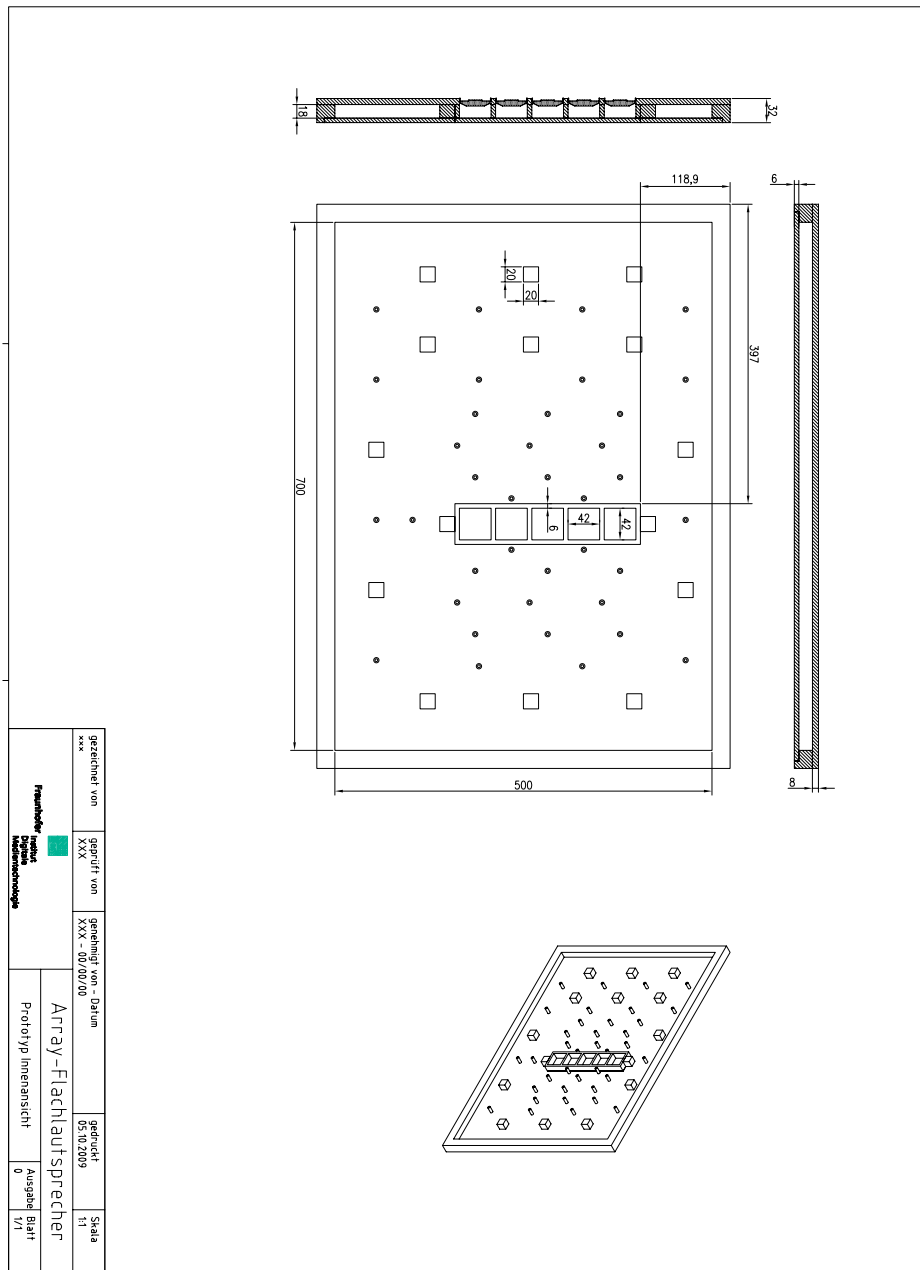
Konstruktionsskizze des gefertigten Flachlautsprechers in der Innenansicht
